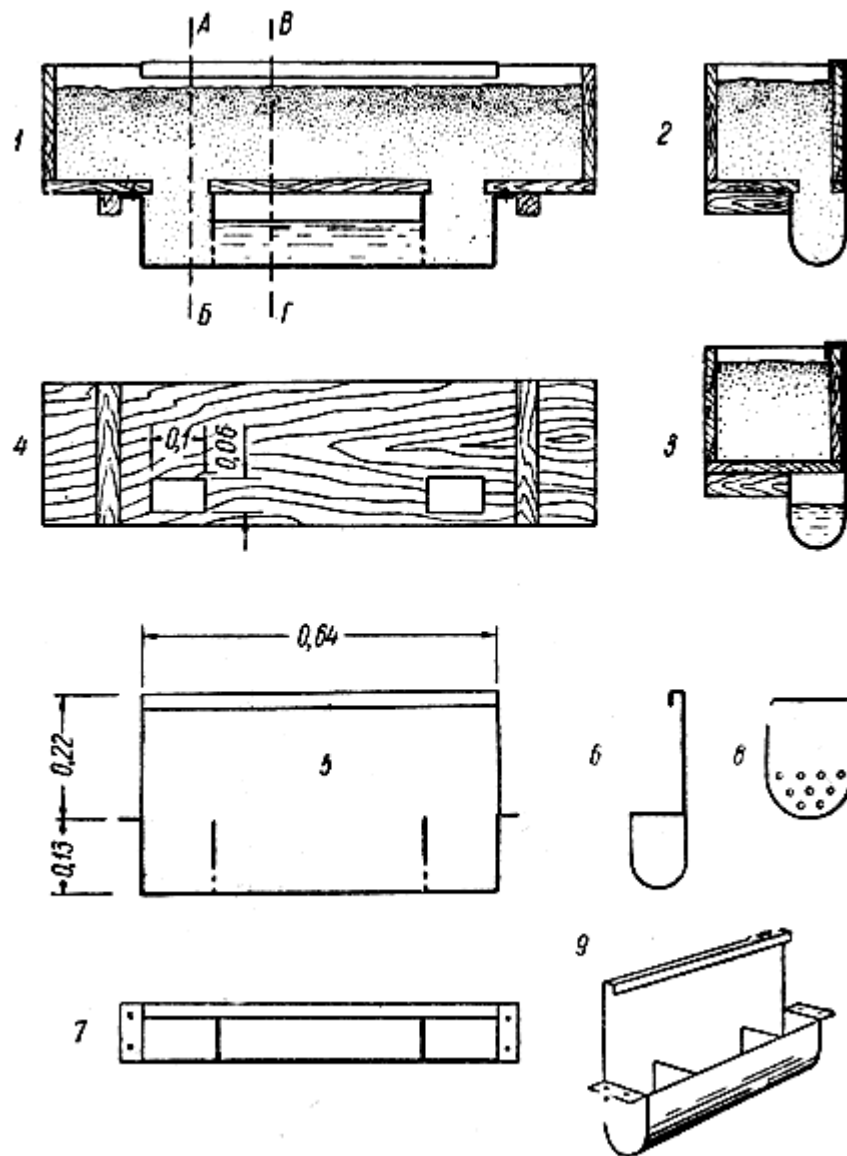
Усовершенствованный цветочный ящик (размеры даны в метрах): 1 - продольный разрез, 2 — поперечный разрез по АБ, 3 - поперечный разрез по ВГ, 4 — вид снизу; резервуар для избыточной влаги: 6 — продольный разрез, 6 — поперечный разрез, 7 — вид сверху, 8 — устройство внутренних перегородок резервуара, 9 — общий вид резервуара
